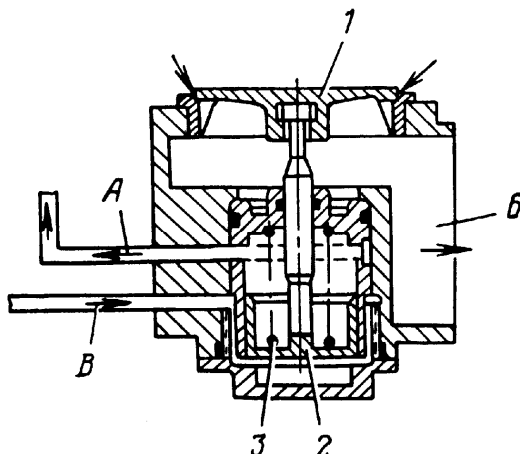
Клапан перепуска воздуха (конструктивная схема):
